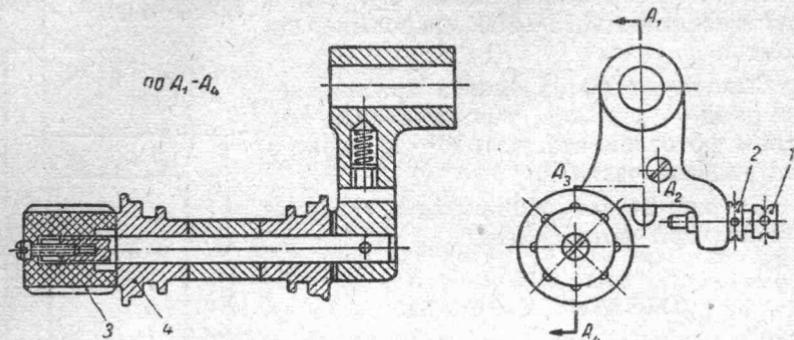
Каретка: 1 — винт; 2 — контргайка; 3 — рукоятка;
